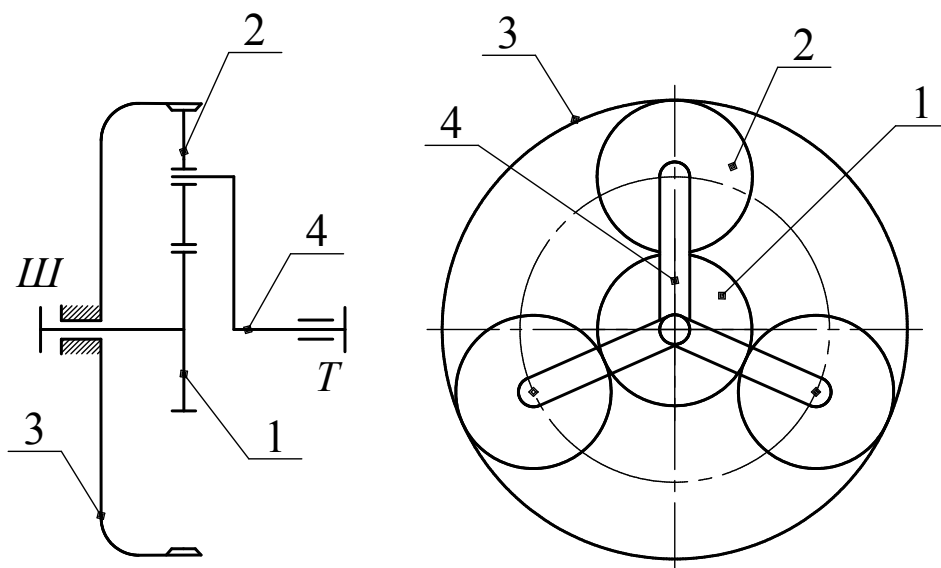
Кинематическая схема планетарного редуктора:
